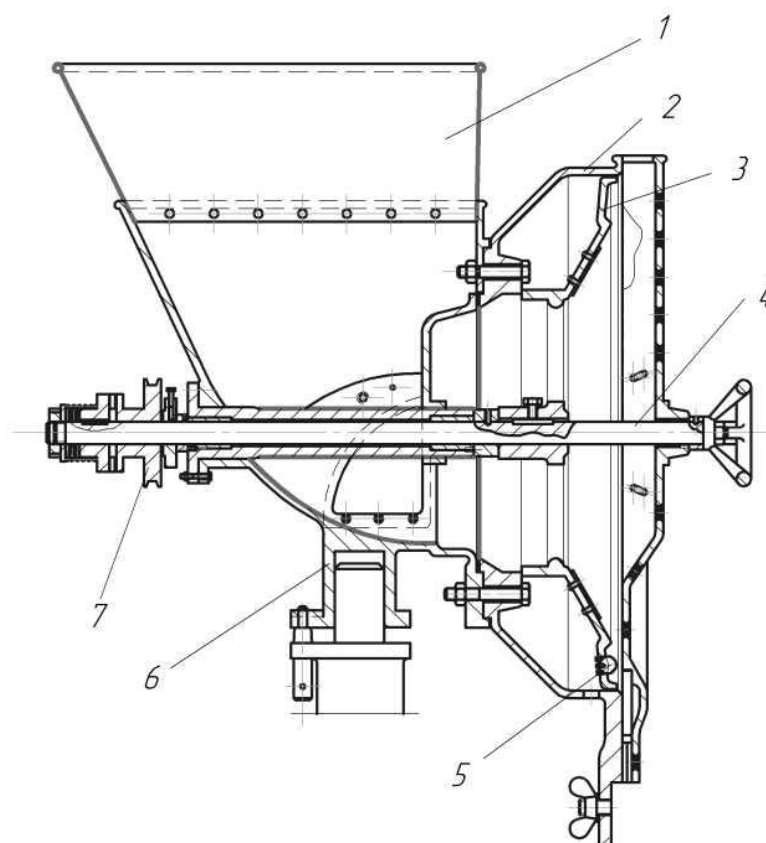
Механічний дисковий вертикальний бункерний завантажувальний пристрій для кронен–пробок:
